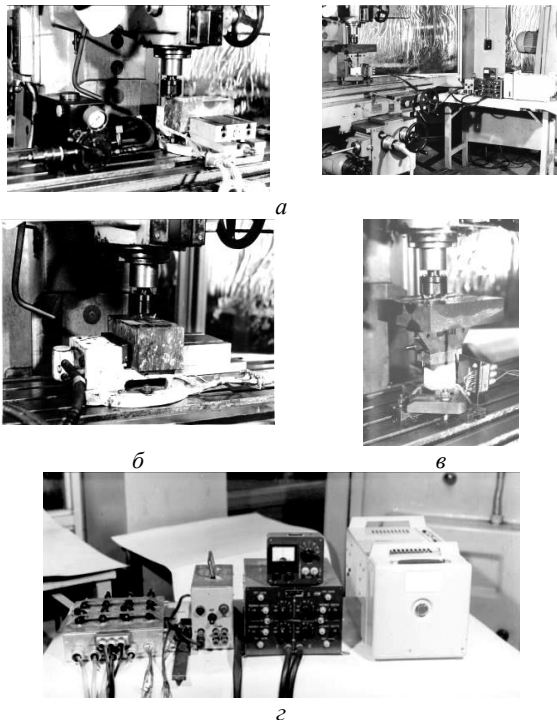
Рабочие моменты проведения исследования динамических процессов при обработке деталей на вертикально-фрезерном станке ВМ-127: *а* - рабочие моменты испытаний; *б* - станочное приспособление тисочного типа; *в* - приспособление из деталей комплекта УСП; *г* - аппаратура для проведения тензометрических исследований: усилитель ТА-5; осциллограф светолучевой НО41; переключатель датчиков
